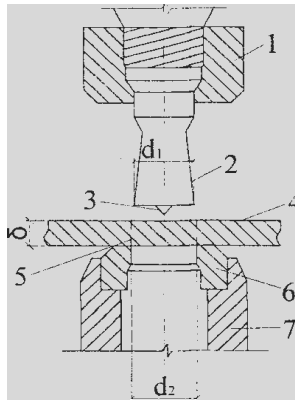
Схема пробивання отворів: 1 - гайка для кріплення пуансона; 2 - пуансон; 3 - конус; 4 - прокатна сталь; 5 - площина відколу; 6 - матриця; 7 - подушка
